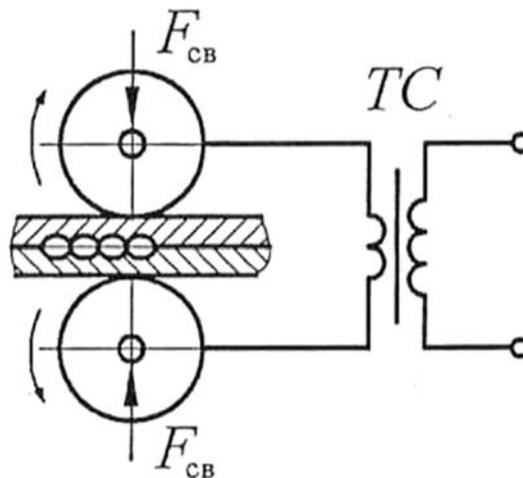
Упрощенная схема процесса контактной шовной сварки
